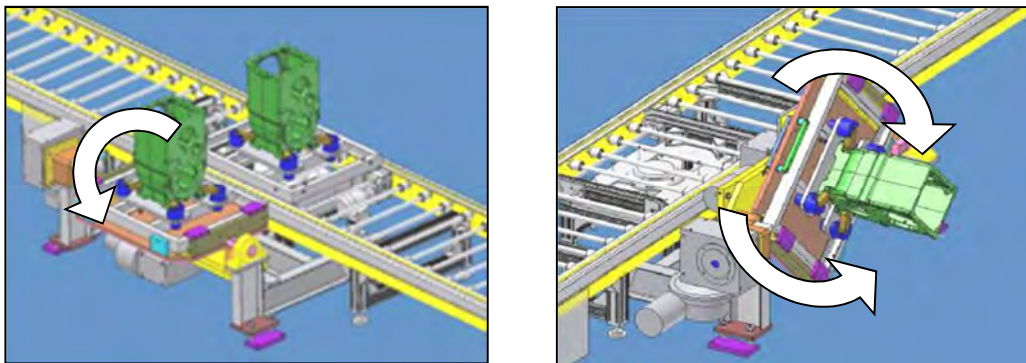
B MOVIMIENTOS DEL VOLTEADOR.
